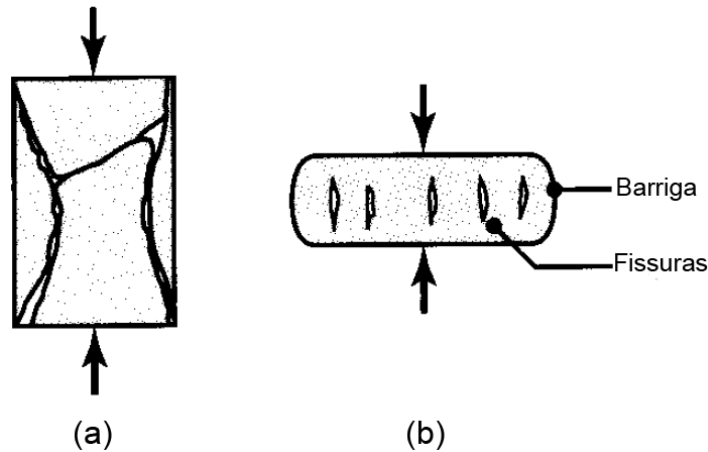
Exemplo do aparecimento de fissuras no teste de compressão, adaptado de (Kalpakji 2014).
